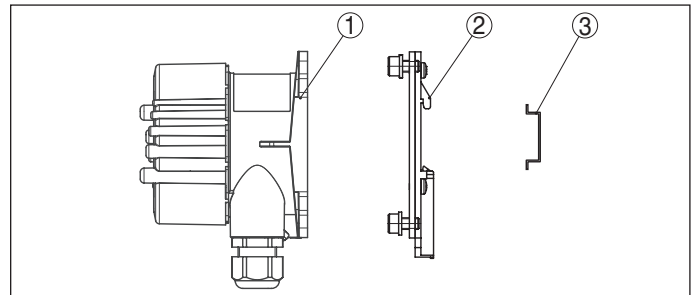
VEGADIS avec boîtier en aluminium ou acier inox pour le montage sur rail
